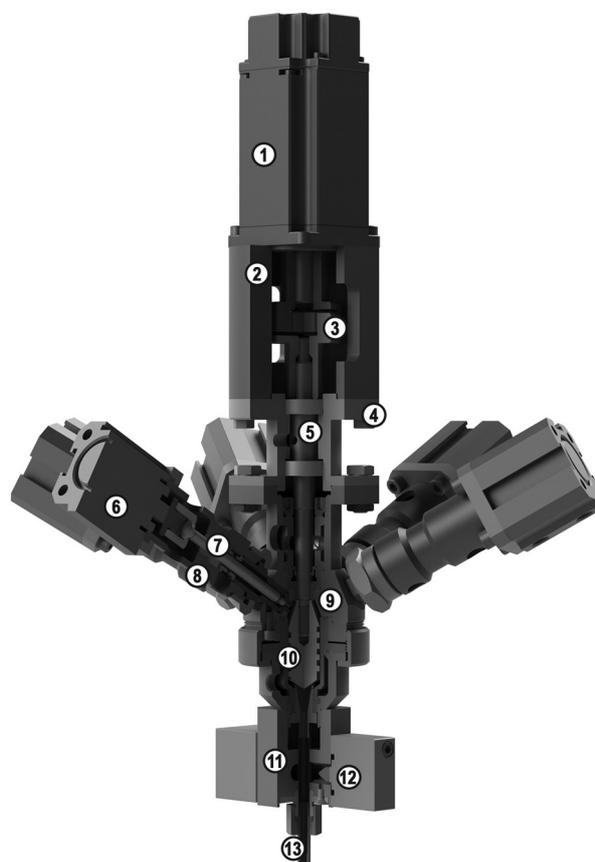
Смесительное устройство низкого давления: 1 – серводвигатель; 2 – стакан; 3 – муфта; 4 – корпус подшипников; 5 – вал с подшипниками; 6 и 12 – пневмоцилиндр; 7 – плунжер; 8 – клапан; 9 – корпус; 10 – ротор; 11 – отсекатель; 13 – сопло
